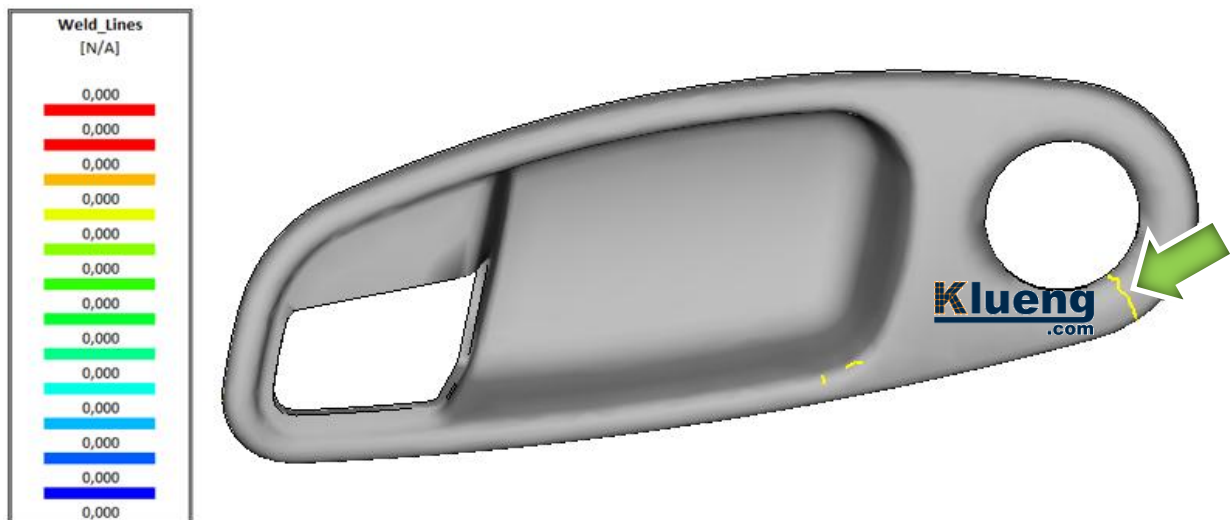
Nueva posición de la línea de soldadura
